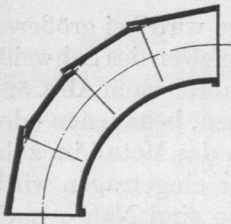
Geschweißter Krümmer. W. Fitzner, Laurahütte.
